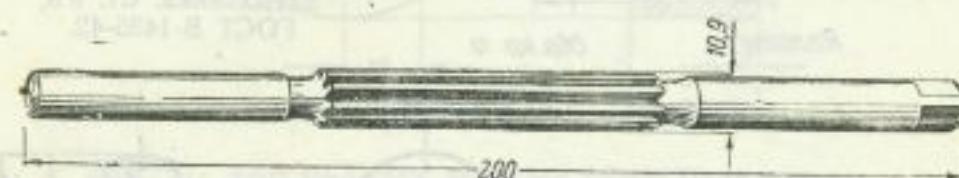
Развёртка с направлением для развёртывания отверстий в ушках дна короба $\frac{Д-И}{ПМ-3}$.
